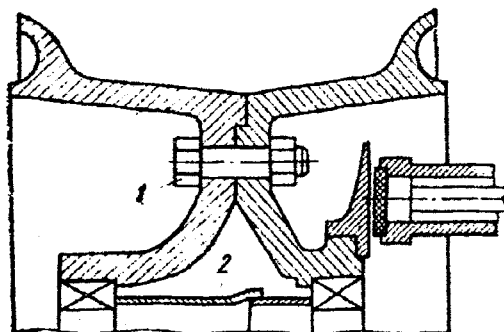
Барабан колеса с осевым разъемом: 1-болты соединения частей барабана; 2-подшипники с распорной втулкой
